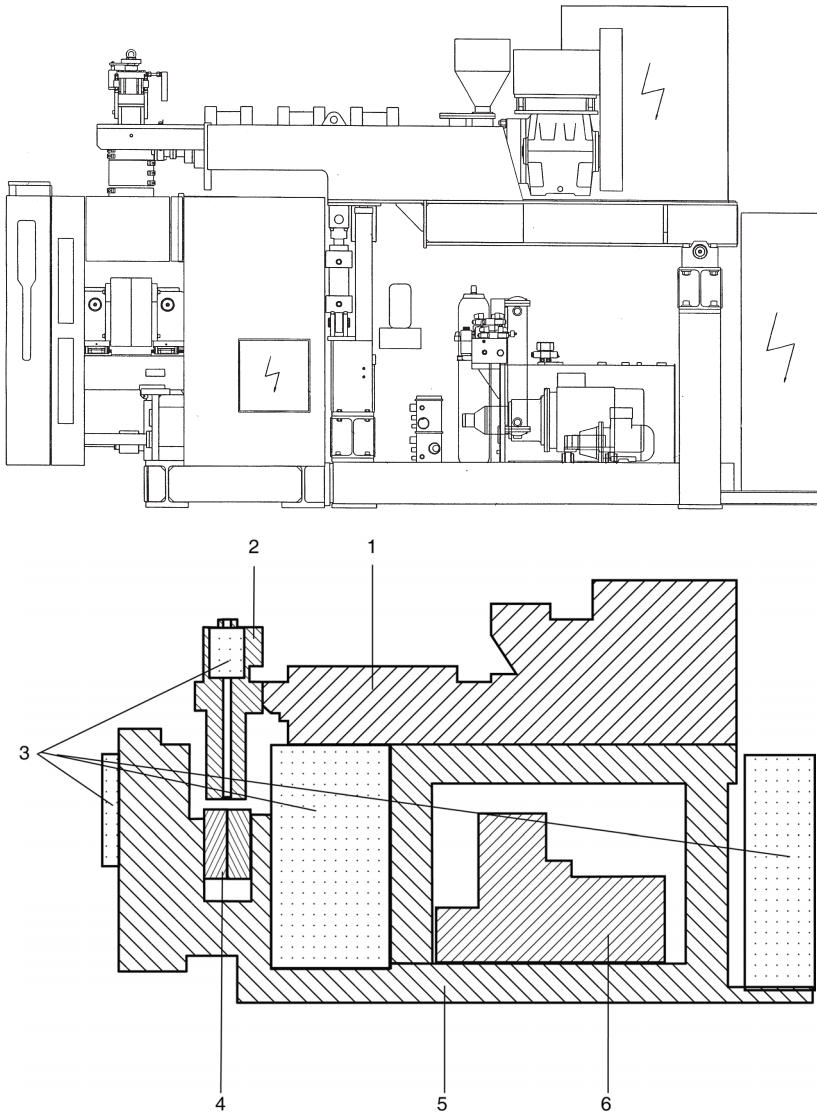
Grundsätzlicher Aufbau einer Extrusionsblasformmaschine (Bild: Kautex Maschinenbau)
